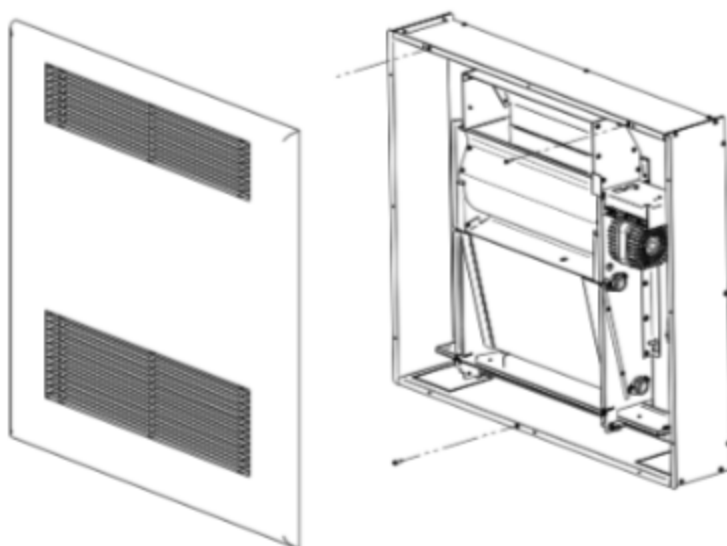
Vista del ventilconvettore ad incasso all'interno della struttura di fissaggio e con pannello di copertura.
